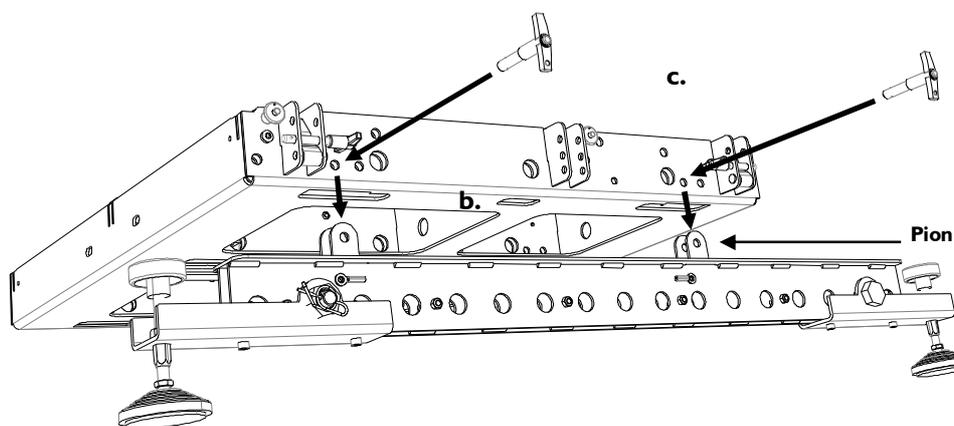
Montage de la plateforme (exemple en extension arrière)
